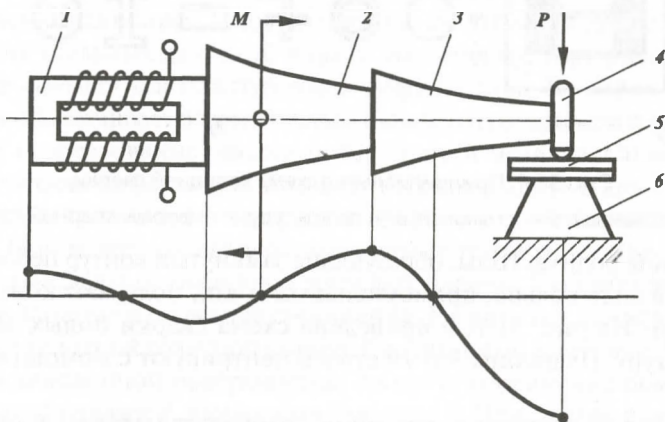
Принципиальная схема ультразвуковой сварки
